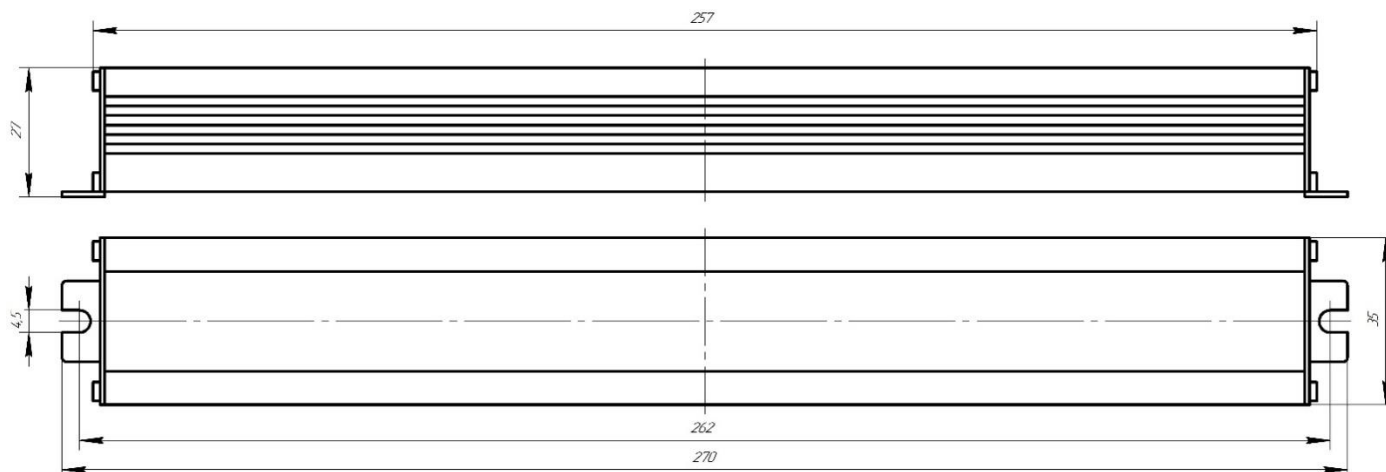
Габаритные размеры Star 100-700T Industrial, Star 130-700T Industrial
